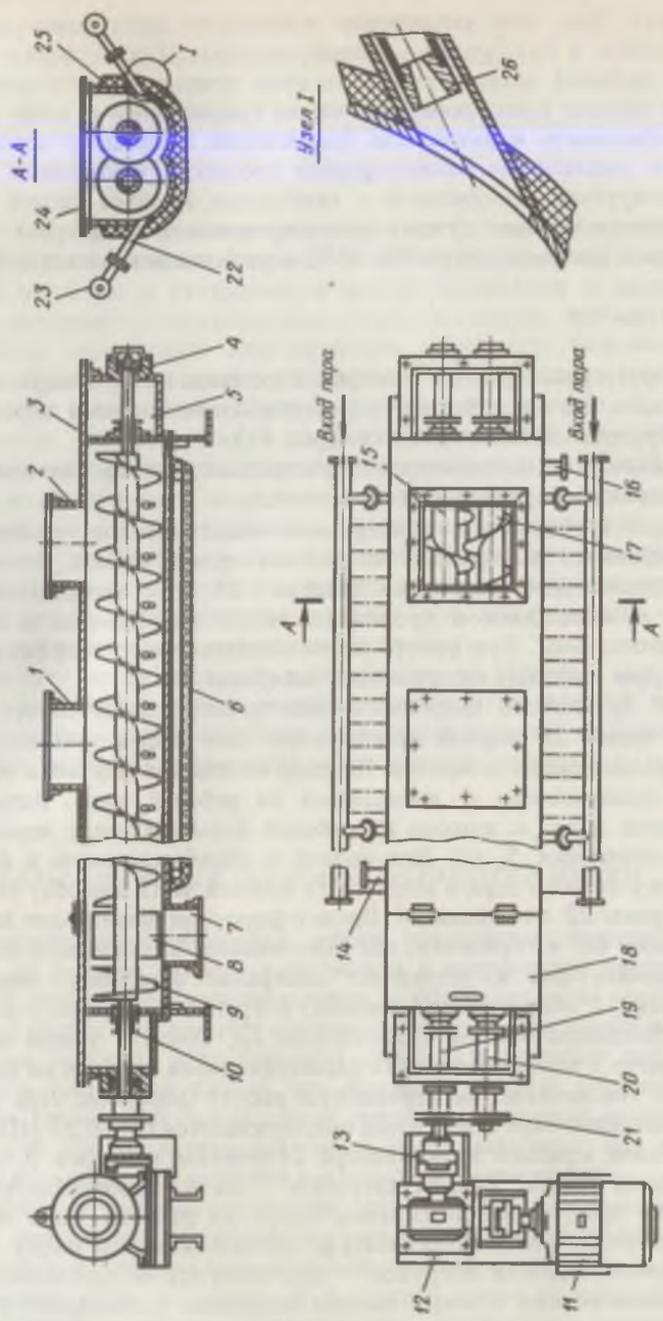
Групповой шнековый инактиватор (пропарочно-увлажнительный шнек)
